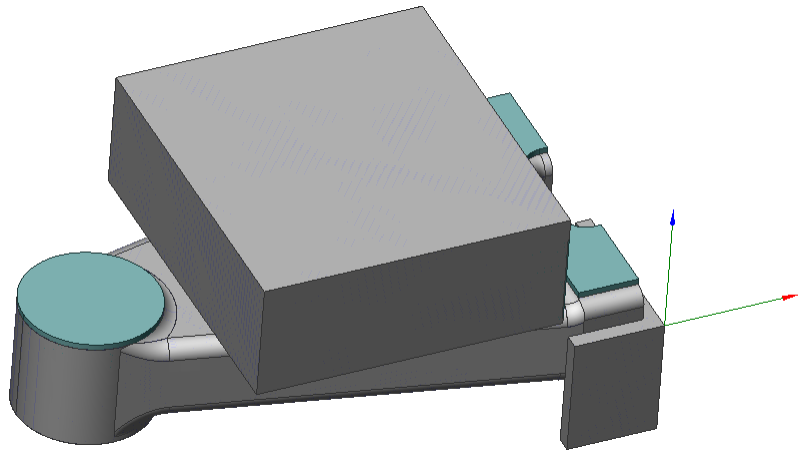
Базування та нульова точка координат заготовки при Базуванні 2
